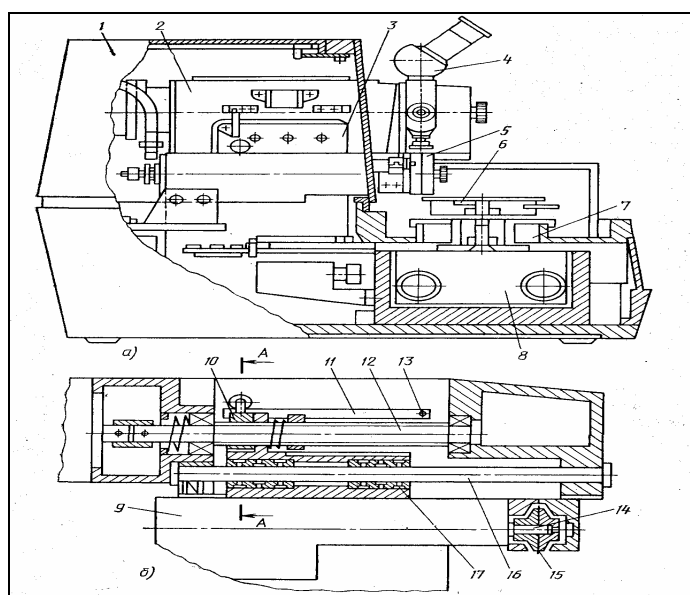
Установка разделения пластин алмазными кругами
